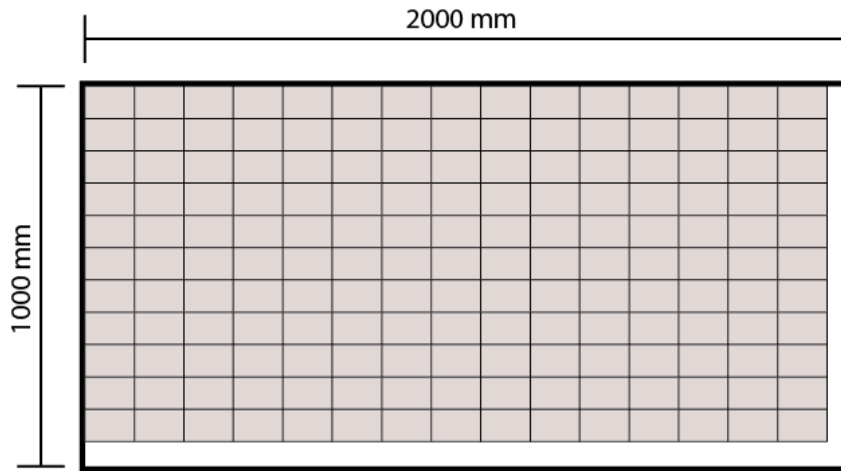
Cortes de las piezas “agarraderas de boleó” en una plancha de grilon
